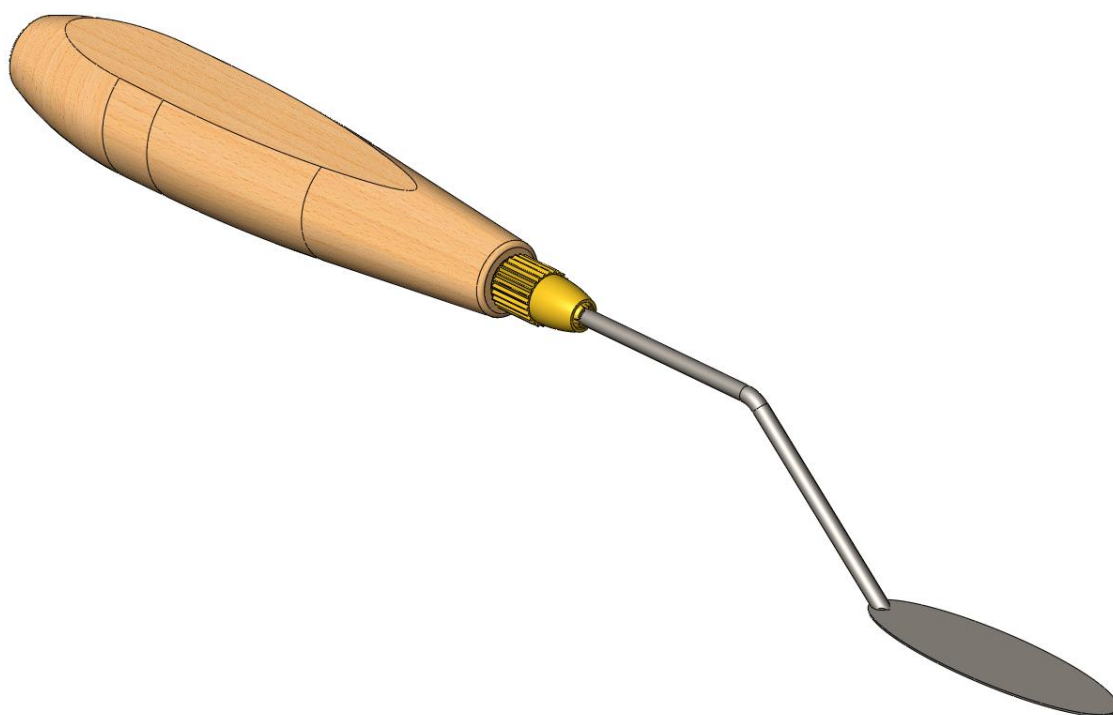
Модель с деревянной ручкой округлой формы, креплением дужки в рукоять цангой и соединением лезвия с дужкой контактно-точечной аргано-дуговой сваркой.
